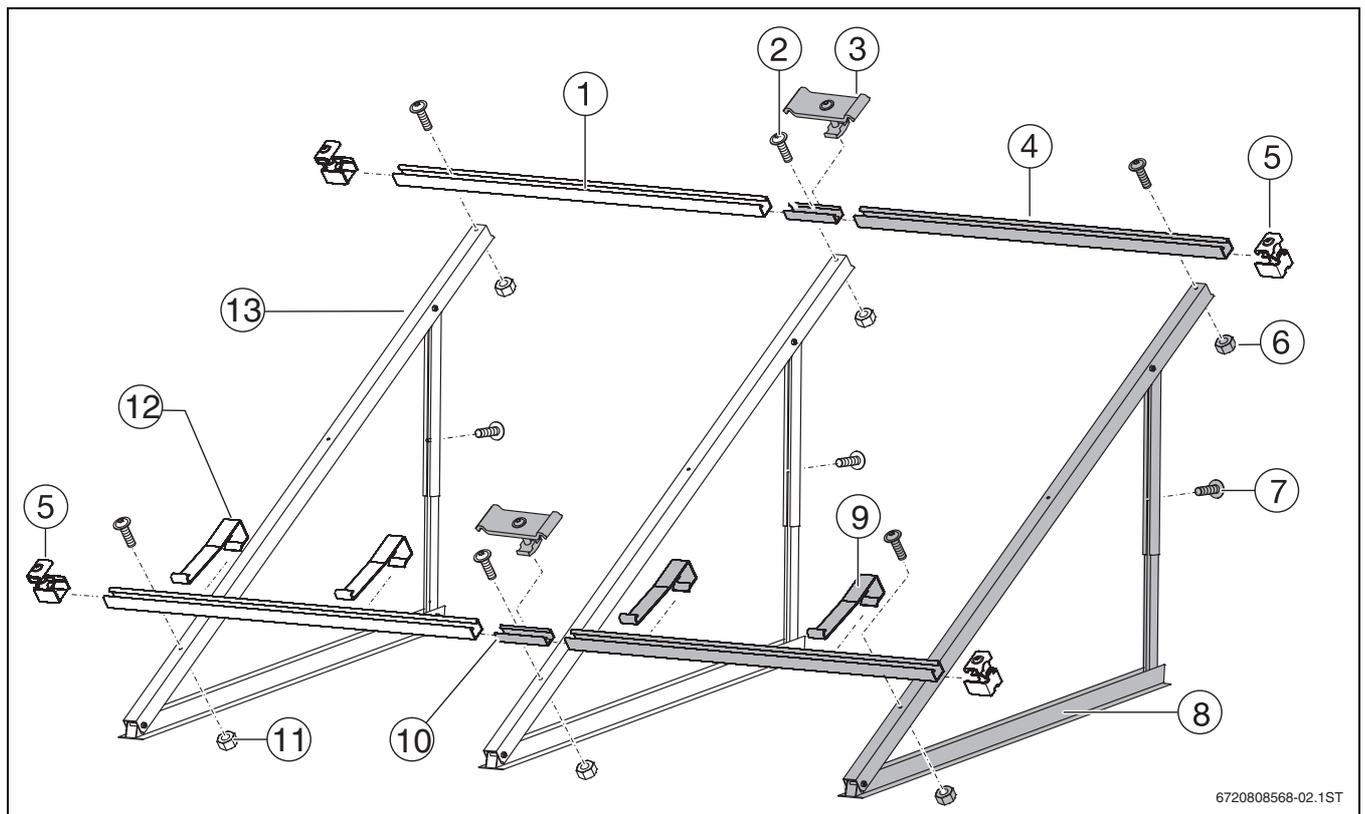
Montage-Set für 2 Kollektoren: 1 Montage-Set Grundauführung, 1 Montage-Set Erweiterung (grau)
